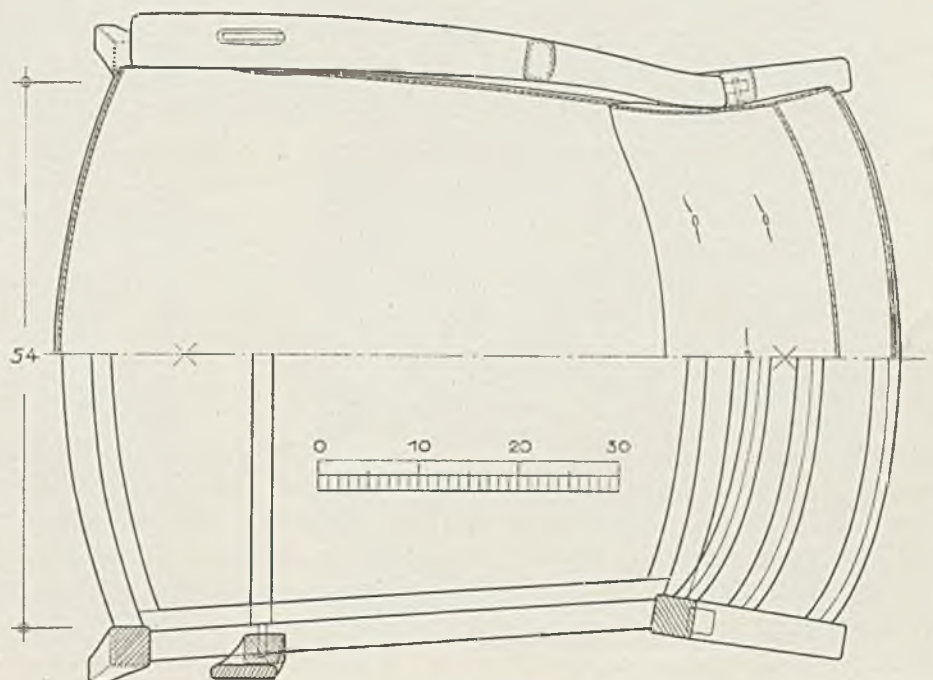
Seitenansicht des Sessels auf Seite 164, die Armlehnstütze ist mittels zweier Holzdübel mit Kopf befestigt (siehe auch Abb. 139)
